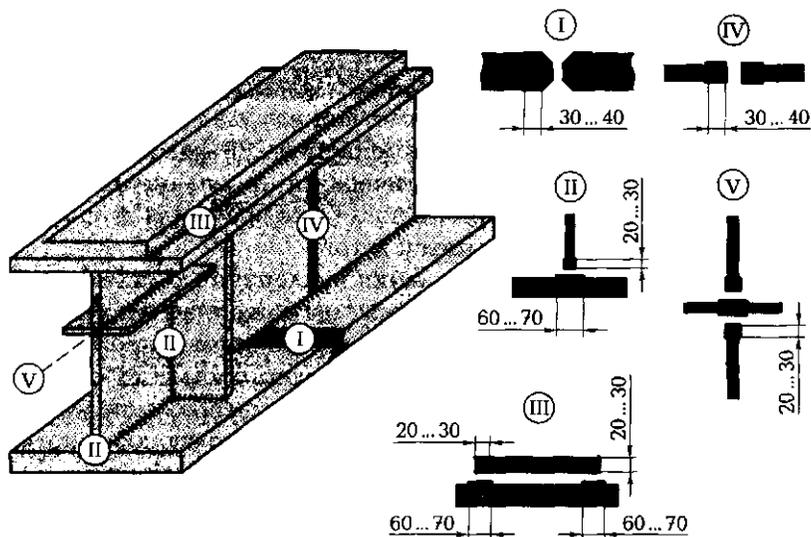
Участки металла, зачищаемые перед сваркой (указаны утолщенной линией), и зоны зачистки перед сваркой: I и IV — стыковые; II и V — тавровые; III — нахлесточное
